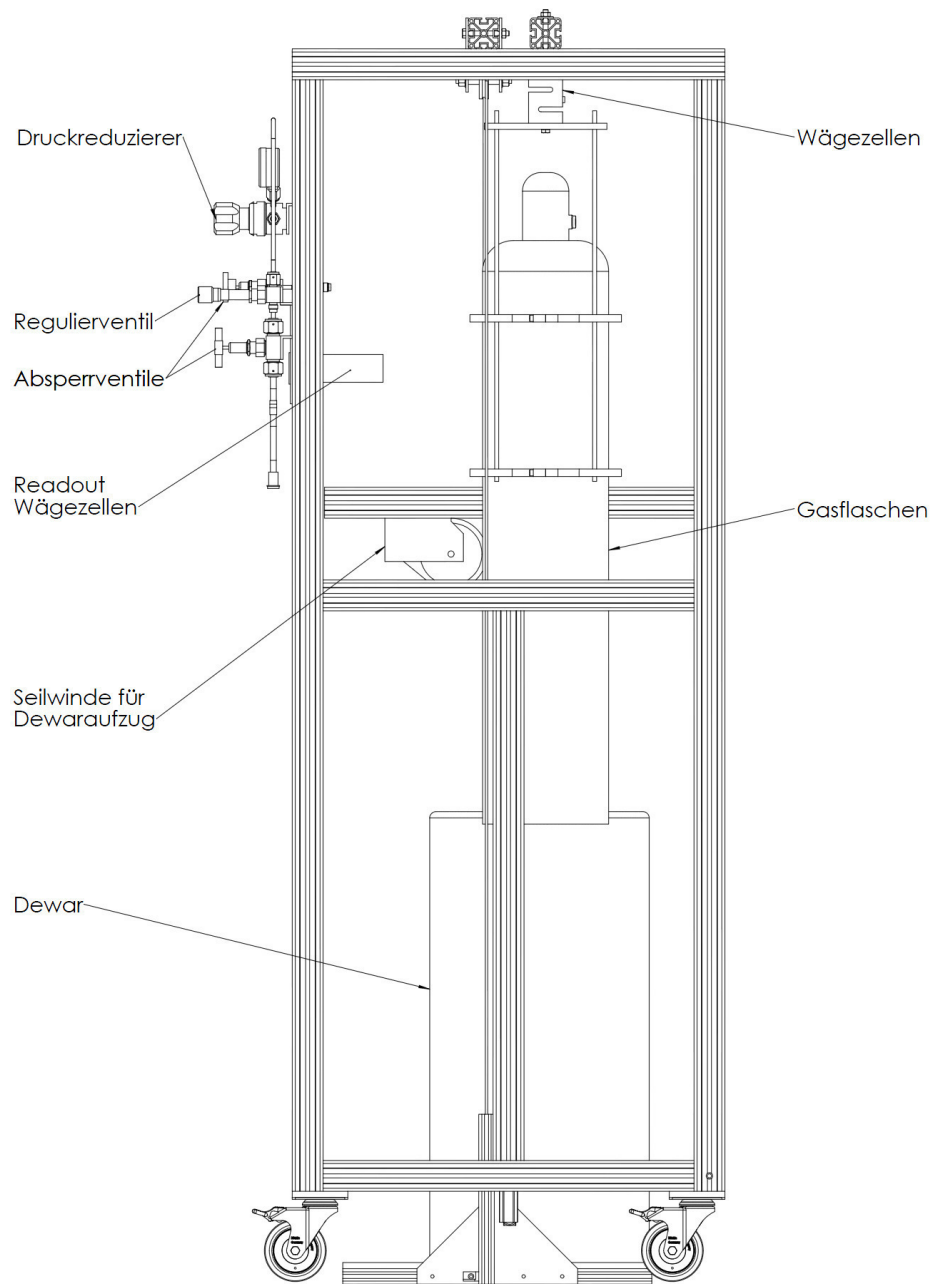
Seitenansicht des Lagersystems mit Bezeichnung der Komponenten.
